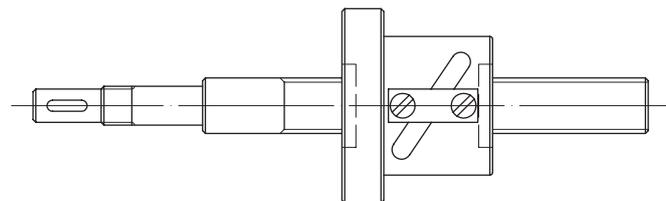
Aufbau eines Kugelgewindetriebe
